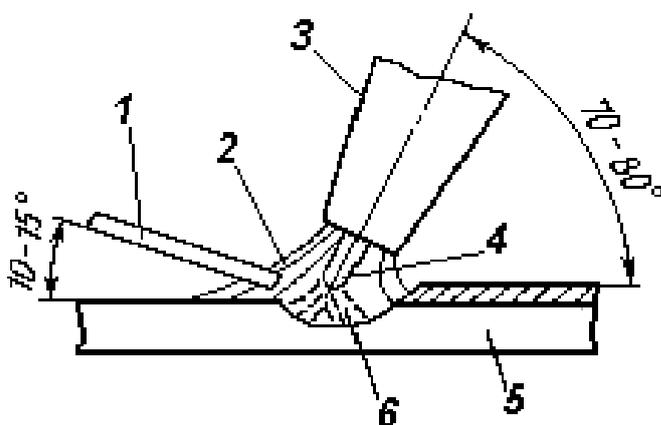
Положение горелки и присадочного прутка при ручной аргонодуговой сварке неплавящимся электродом
